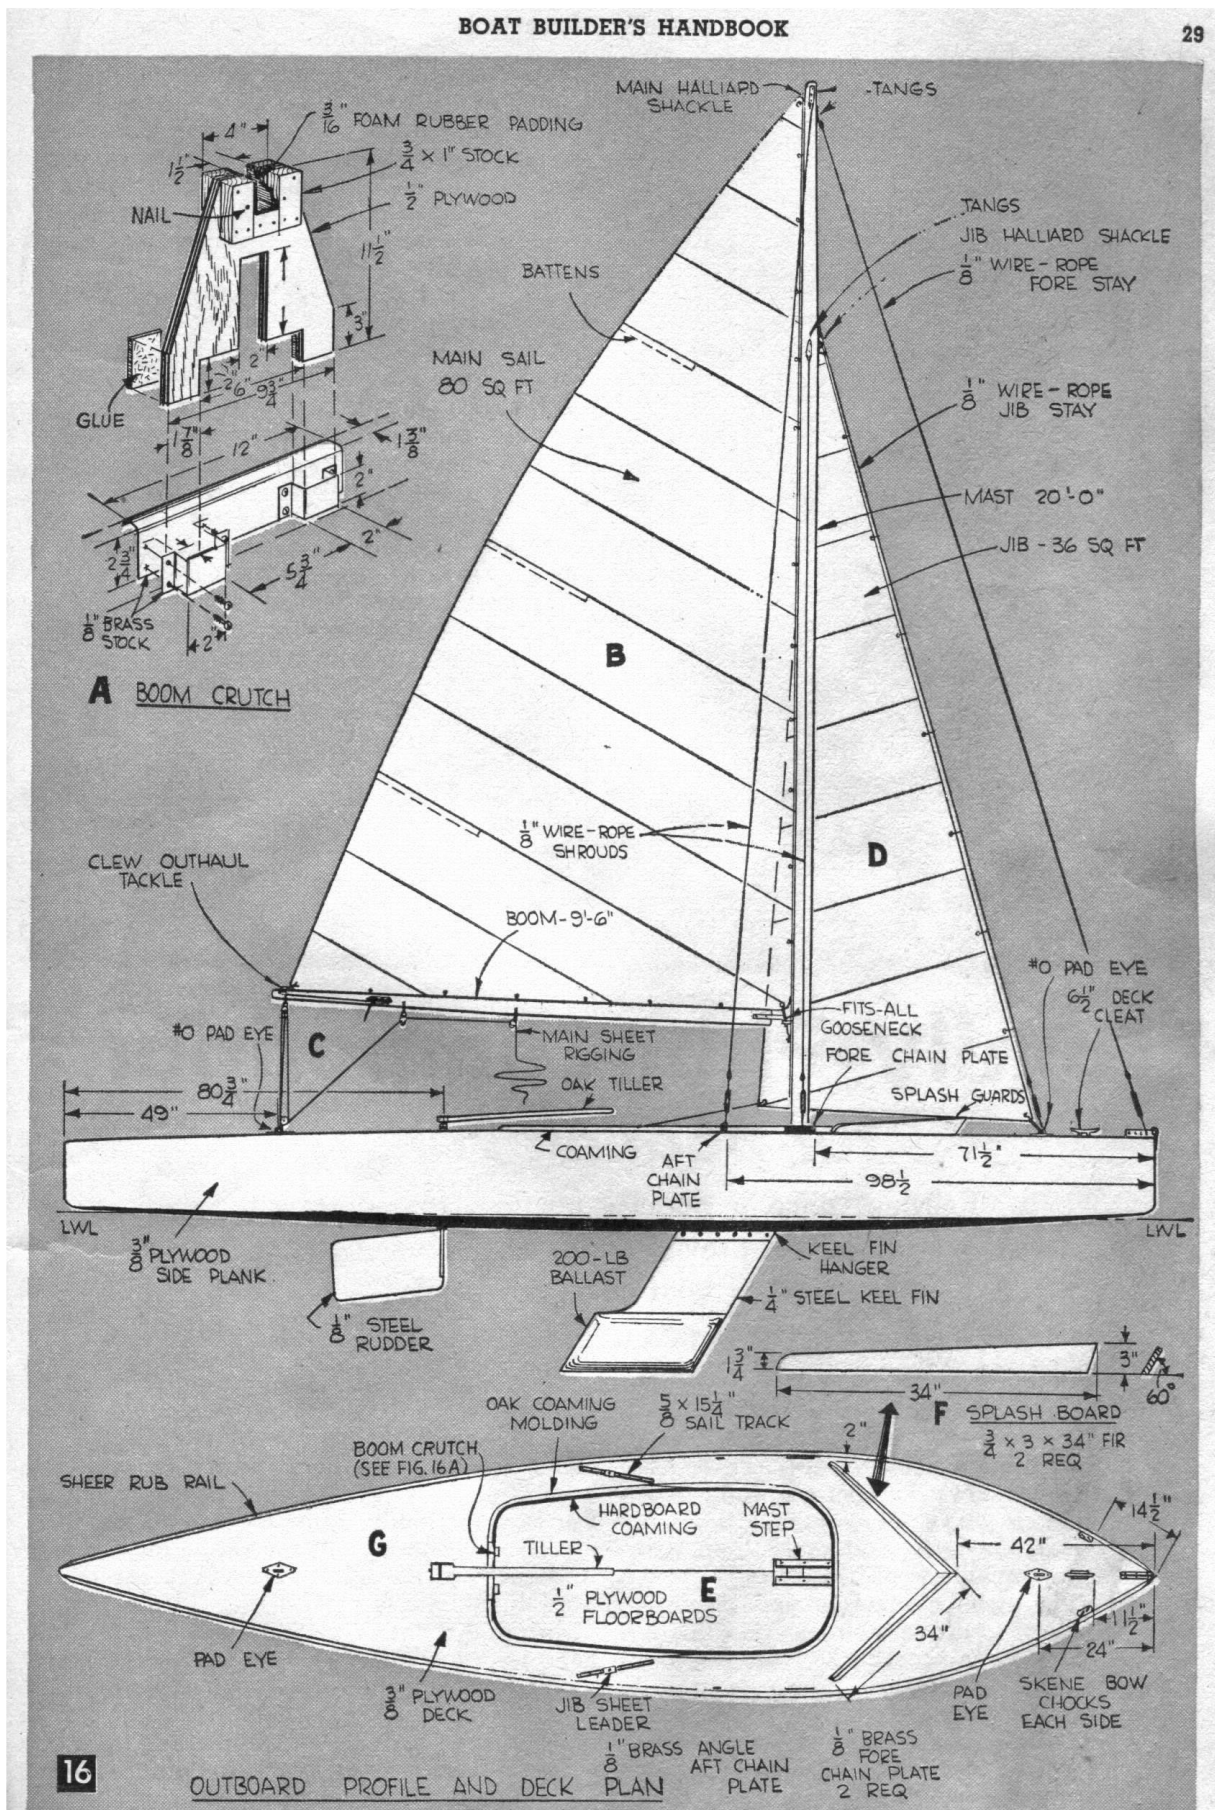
Planos planta y perfil resultado final Missile (Fuente: Svensons.com)
